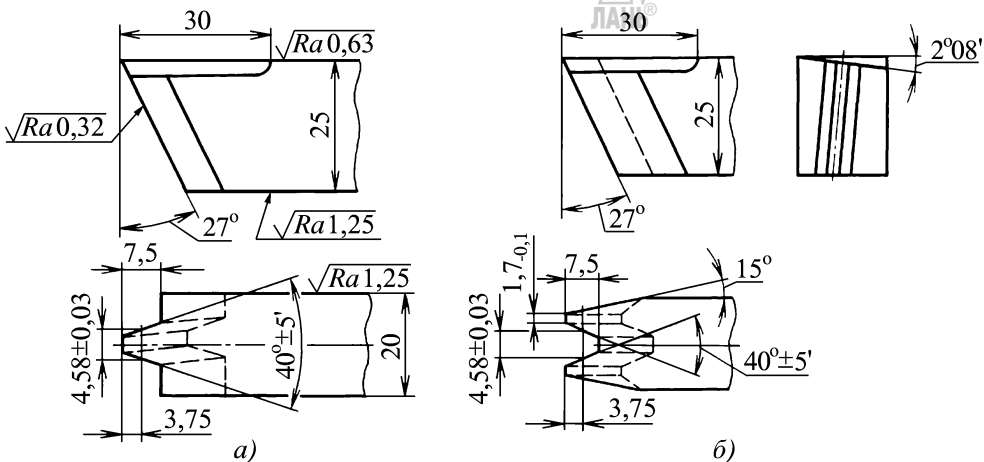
Резцы для затылования фрез с модулем $m \leq 4$:
